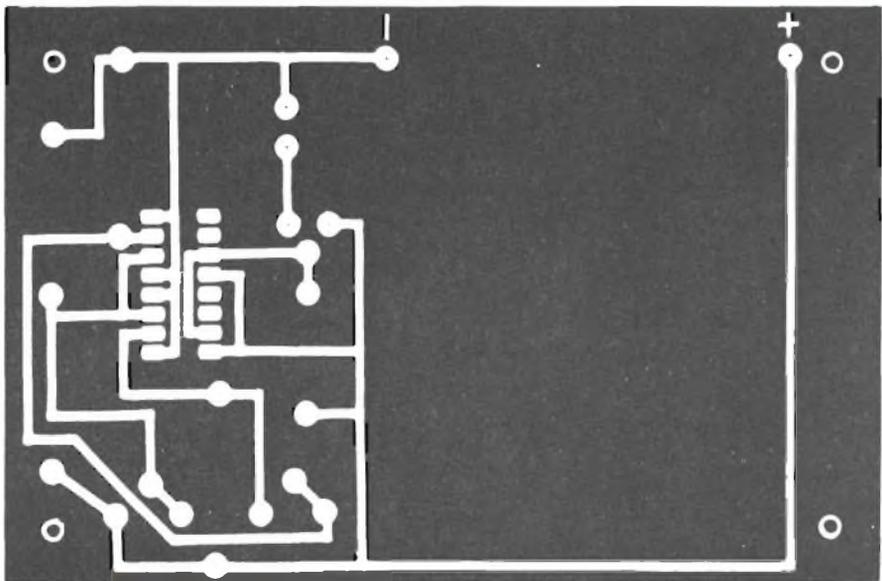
Disegno e piano di foratura del circuito stampato e disposizione dei componenti.
